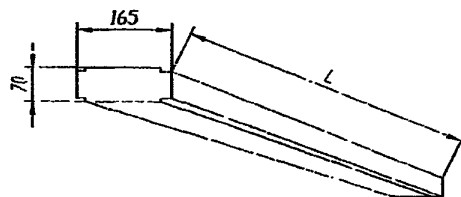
Светильник ЛПО 12-2х20 (L=625 мм)
